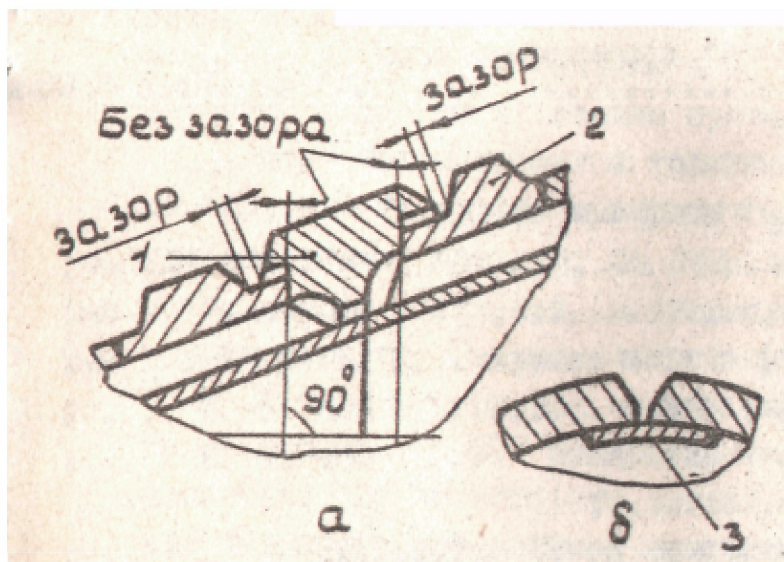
Установка соединительного кольца при сварке секций рубашки корпуса камеры (а) и схема установки подкладки при сварке разъемов этого кольца (б): 1- разъемное соединительное кольцо; 2- переходное кольцо рубашки; 3- подкладка
